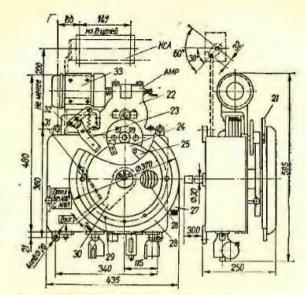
Общий вид пружинного привода типа ГПГМ-10.
